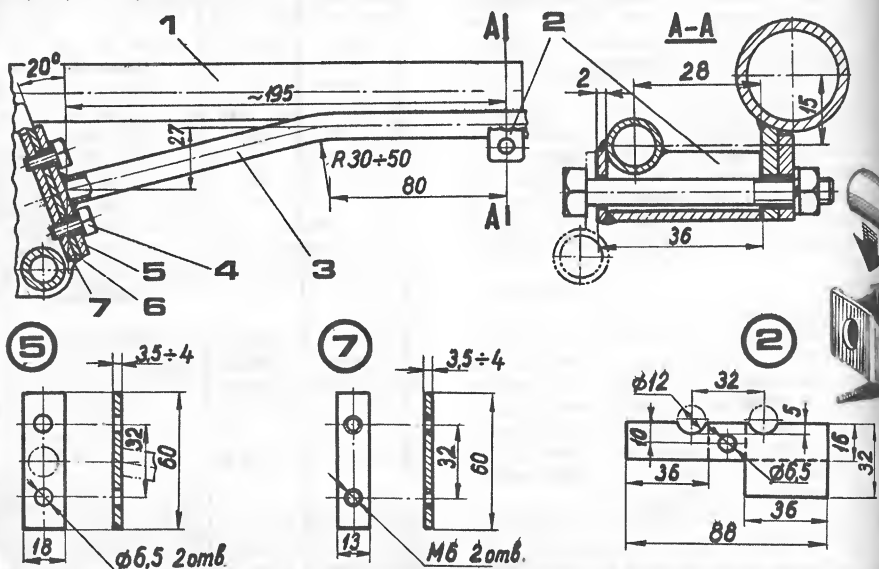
Общий вид багажника: 1 — рама мотоцикла; 2 — рама; 3 — труба багажника; 4 — контур боковой панели; 5 — задний верхний узел крепления
